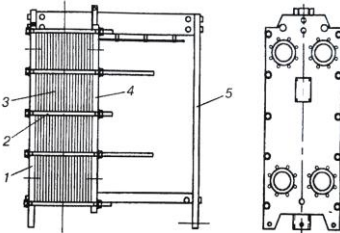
Разборный пластинчатый теплообменник: 1 - нажимная плита; 2 - стягивающие шпильки; 3 - теплопередающие пластины; 4 - нажимная плита; 5 - стойка.
